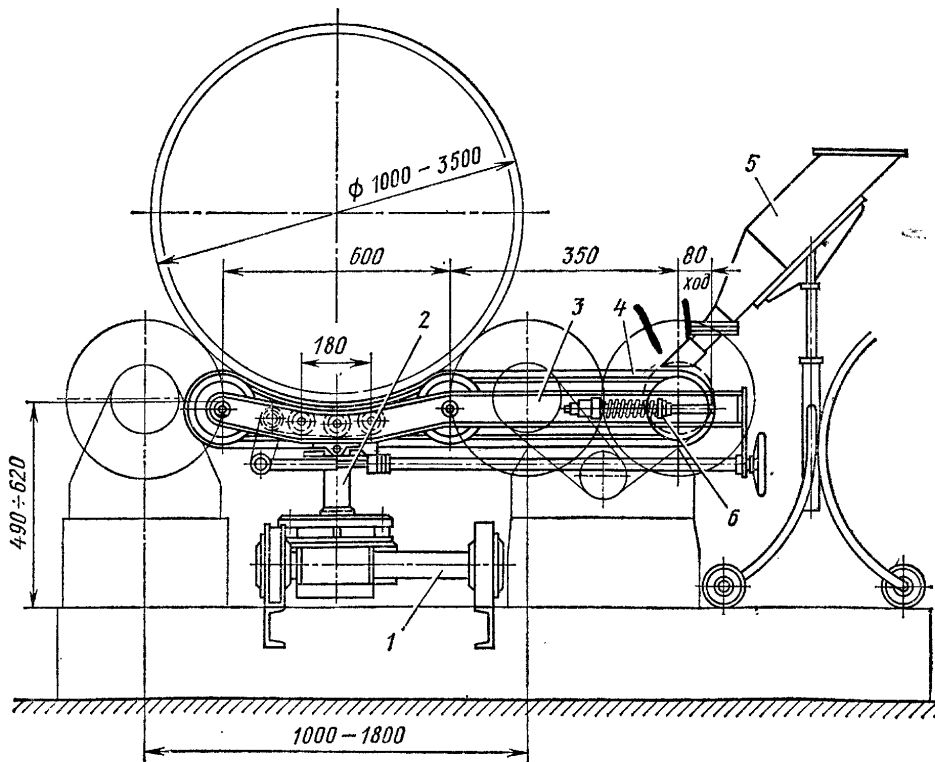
Флюсовая подушка ременного типа для сварки внутренних кольцевых швов:
